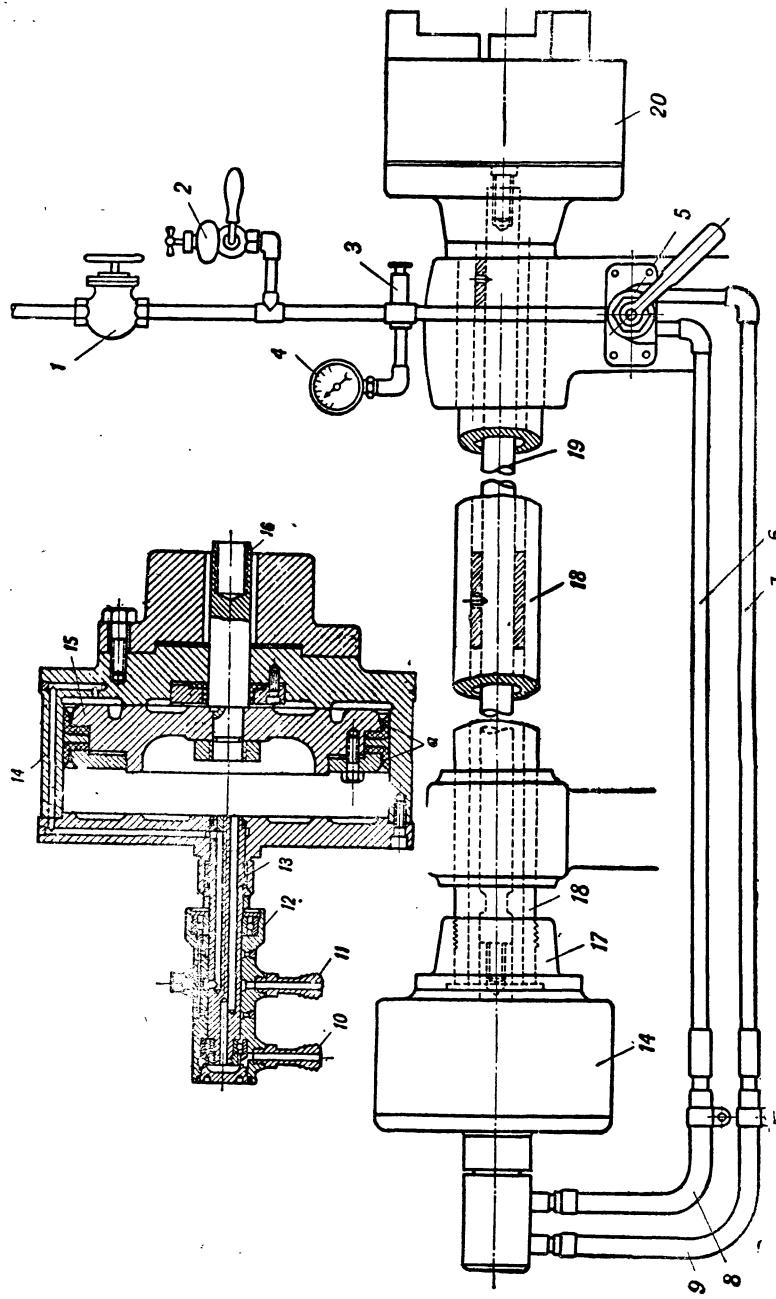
Общий вид установки пневматического патрона. Сверху — разрез воздушного цилиндра.
